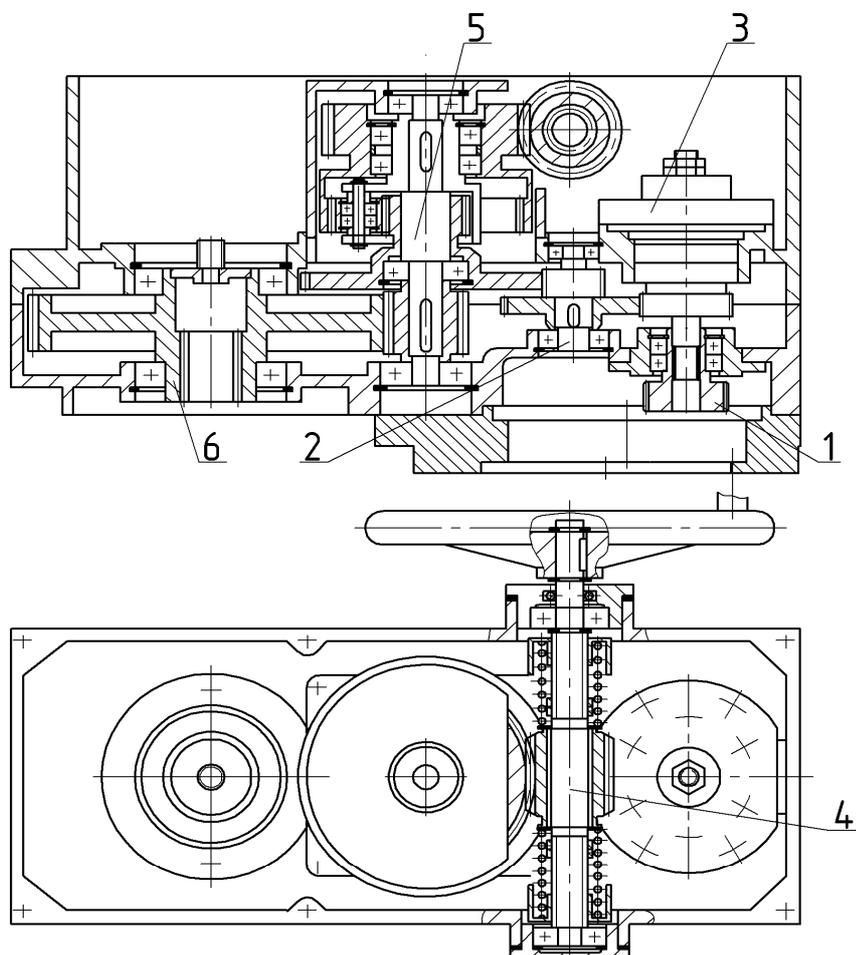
Редуктор механизмов со скоростью штока 10; 6,3; 4; 2,5 мм/с и механизма МЭП-16000/63-63
